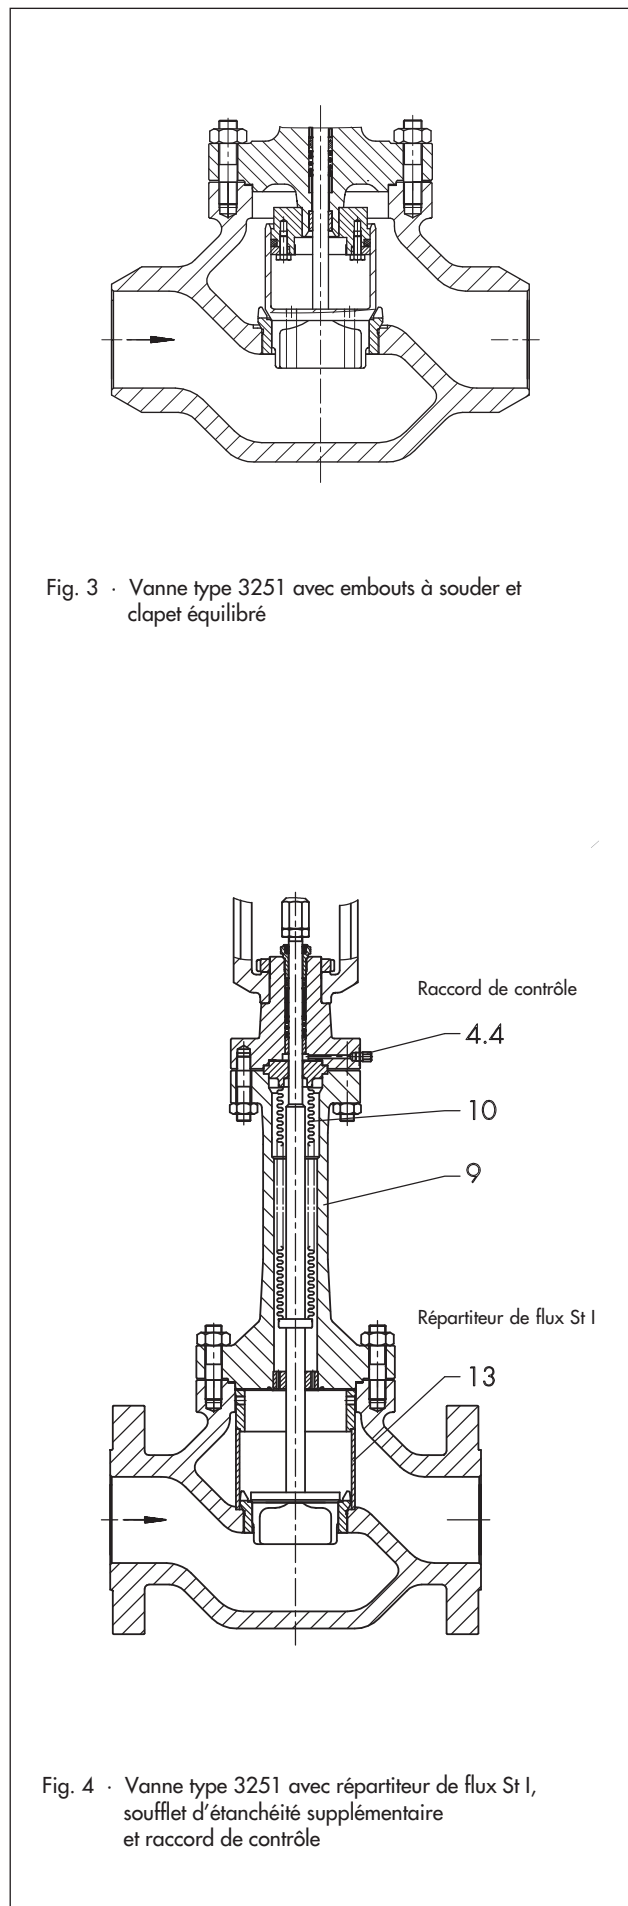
· Vanne type 3251 avec embouts à souder et clapet équilibré
